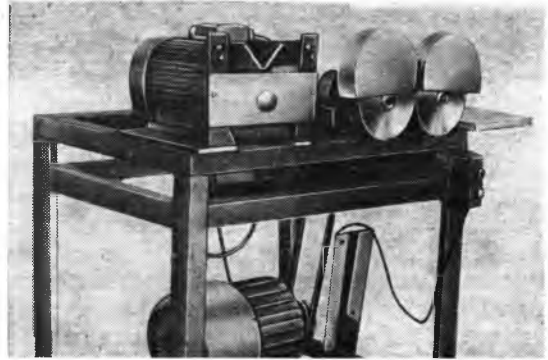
Станок для обжима и заоваливания шипов столярного стула
